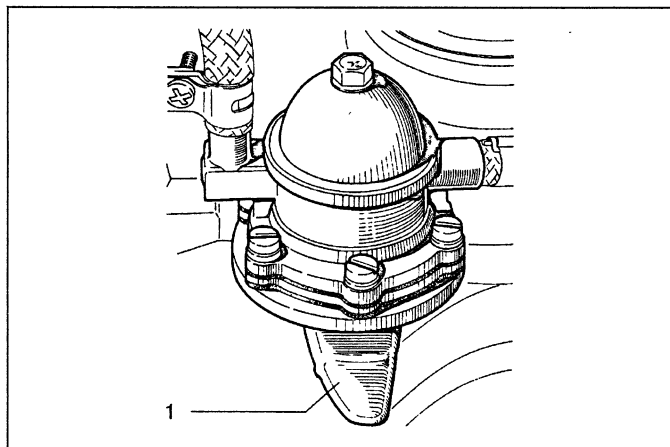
Топливный насос: 1 – рычаг ручной подкачки топлива
